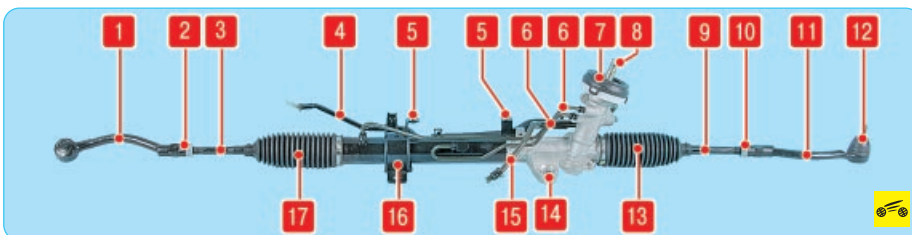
Рулевой механизм: 1, 11 – наконечники рулевых тяг; 2, 10 – контргайки; 3, 9 – рулевые тяги; 4 – обратный трубопровод; 5 – кронштейны крепления термозащиты; 6 – трубопроводы рулевого механизма; 7 – уплотнитель; 8 – вал-шестерня рулевого управления; 12 – палец шарнира наконечника рулевой тяги; 13, 17 – защитные чехлы; 14, 16 – кронштейны крепления рулевого механизма; 15 – напорный трубопровод
